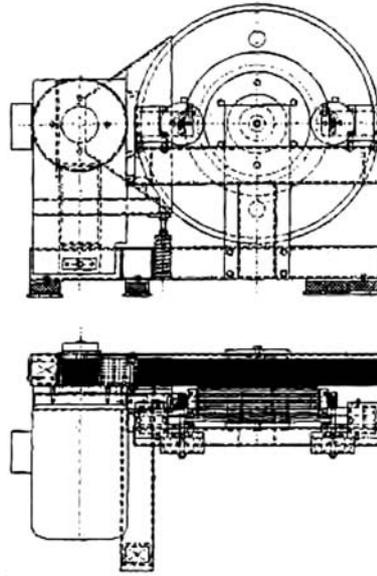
Чертеж лебедки с клиноременным приводом (Ingenieurburo für Aufzugtechnik)
